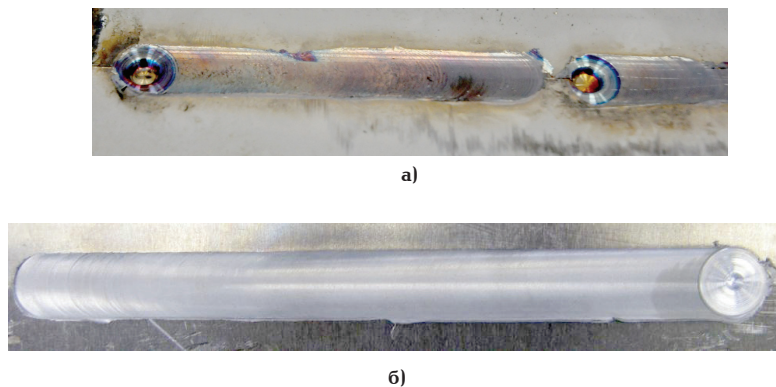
Сварные швы, полученные методом сварки трением с перемешиванием: а — пластины из стали 12Х18Н10Т; б — пластины из алюминиевого сплава АМГ6
